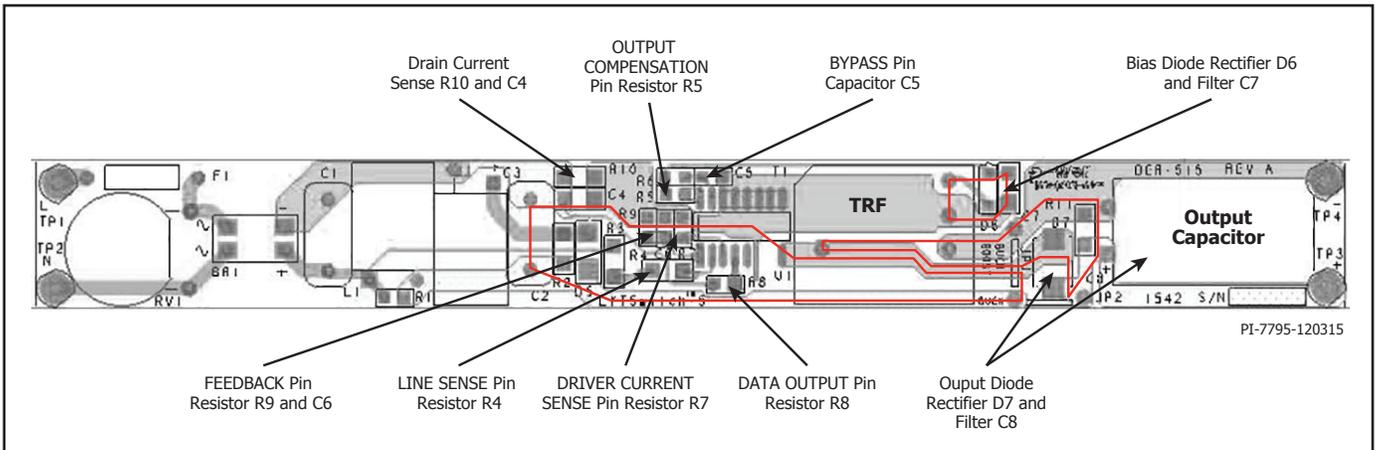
SO-16B D 패키지를 사용하는 DER-515 PCB 레이아웃 예. PCB 레이아웃의 핵심 부품 및 루프 영역 위치를 보여줍니다
